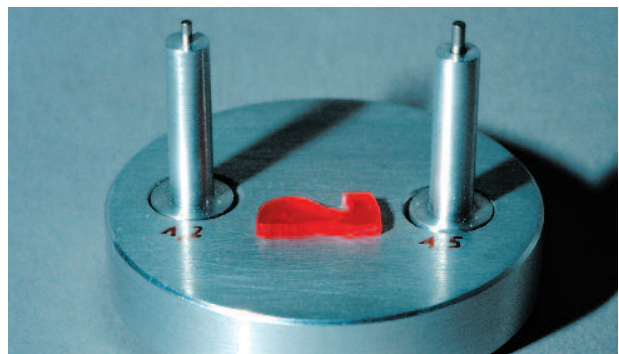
Der Prototyp einer Riegelfräshilfe.
